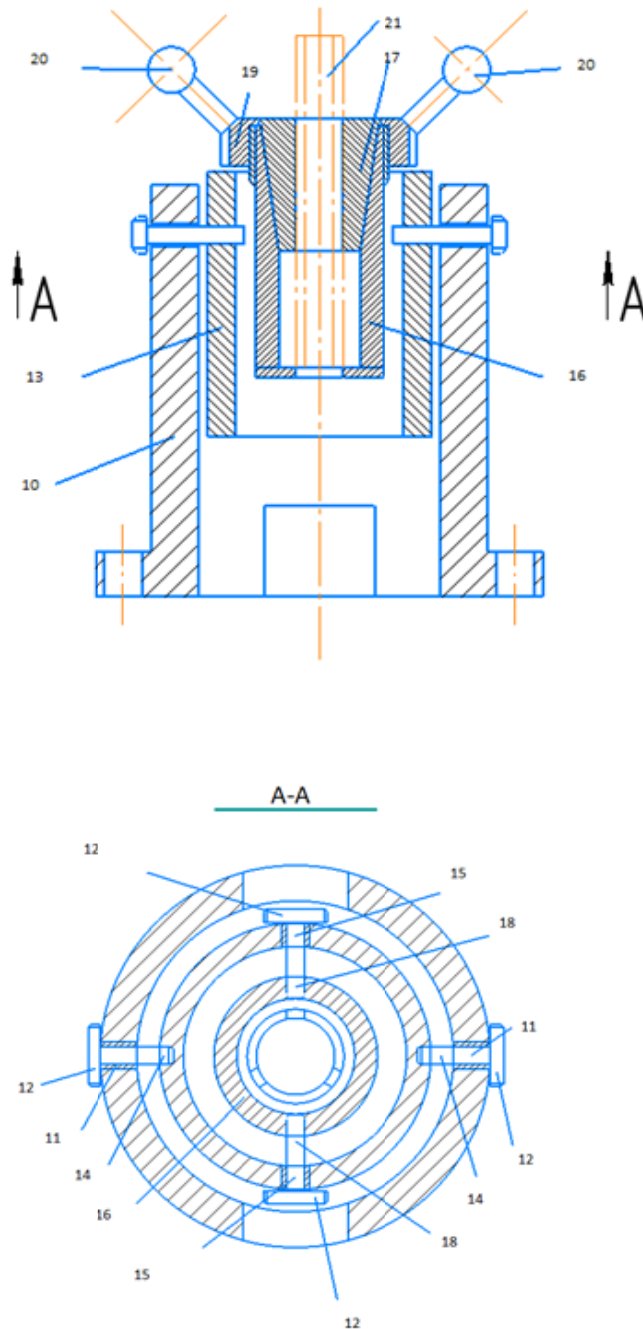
Схема зажимного цангового приспособления для заготовок типа толстостенная втулка с центральным отверстием
